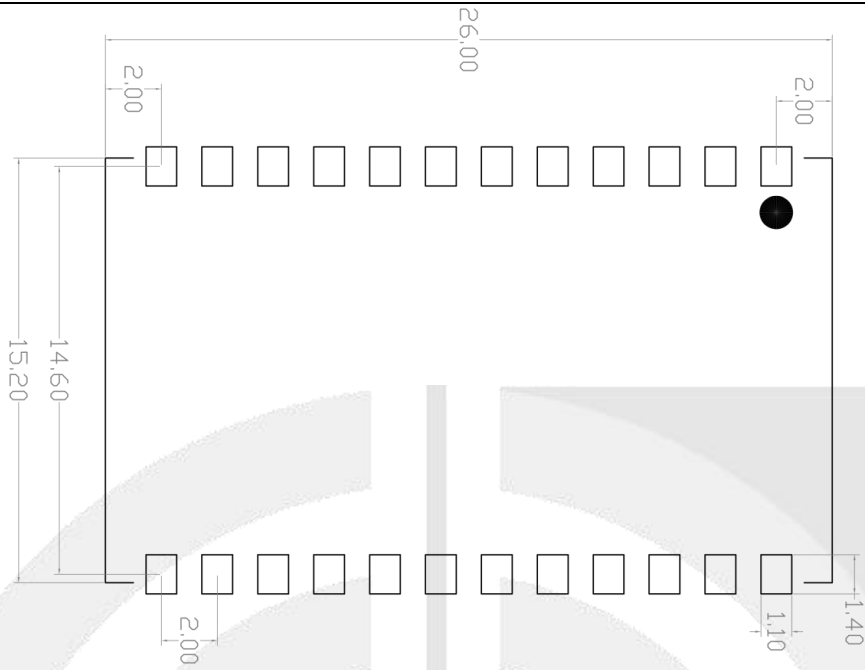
运动姿态传感器微系统芯片 IMU611推荐 PCB 焊盘布局
